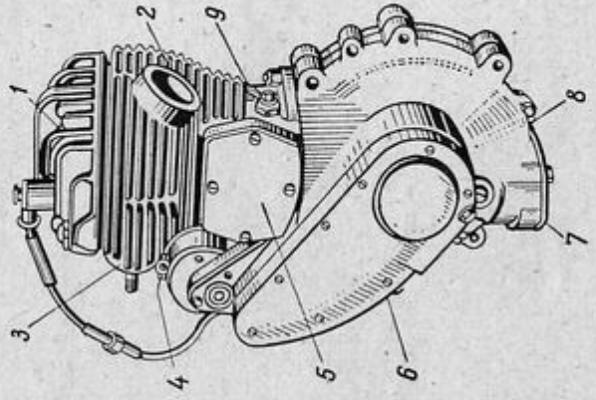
Четырёхтактный однцилиндровый двигатель BSA M-20 с рабочим объёмом 500 см³:
